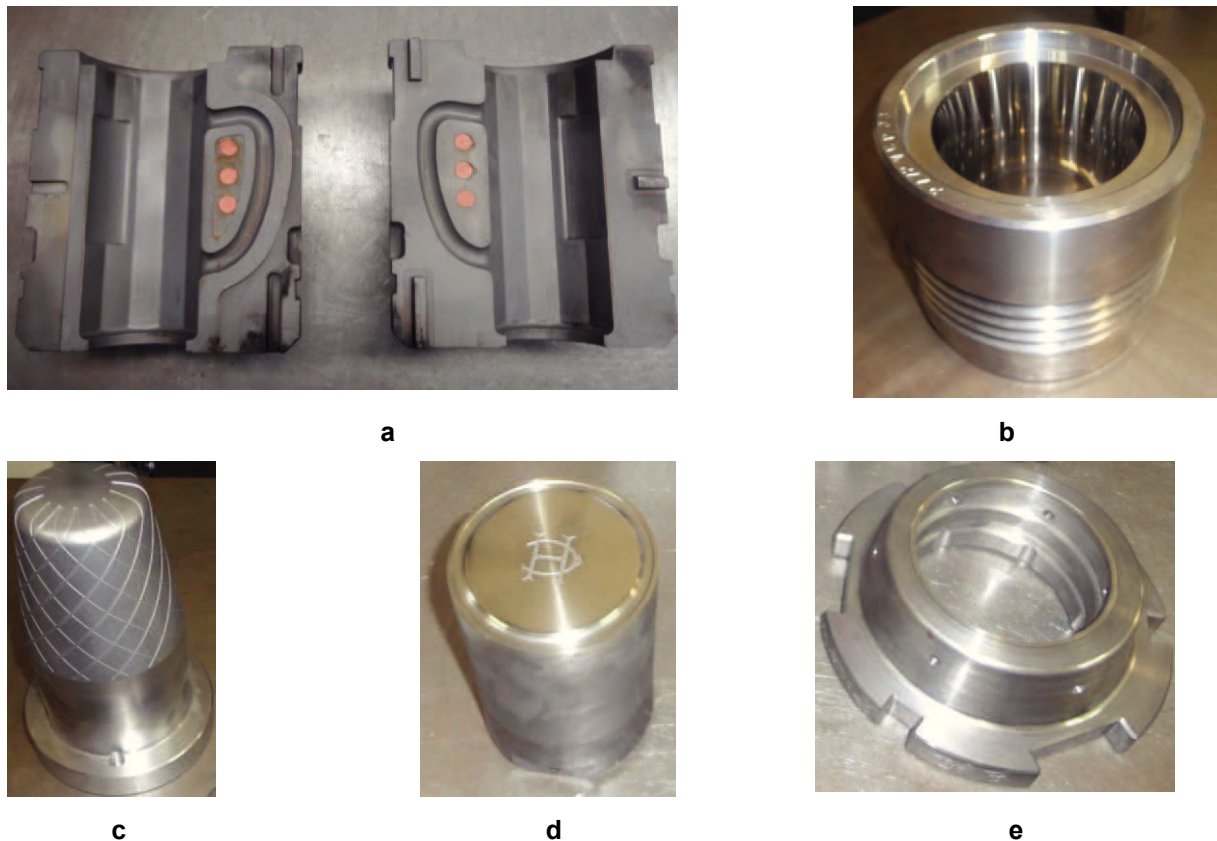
Conjuntos de moldes e acessórios utilizados no processo prensado, a) moldes de abrir, b) molde monobloco, c) punção, d) fundo e e) anel
